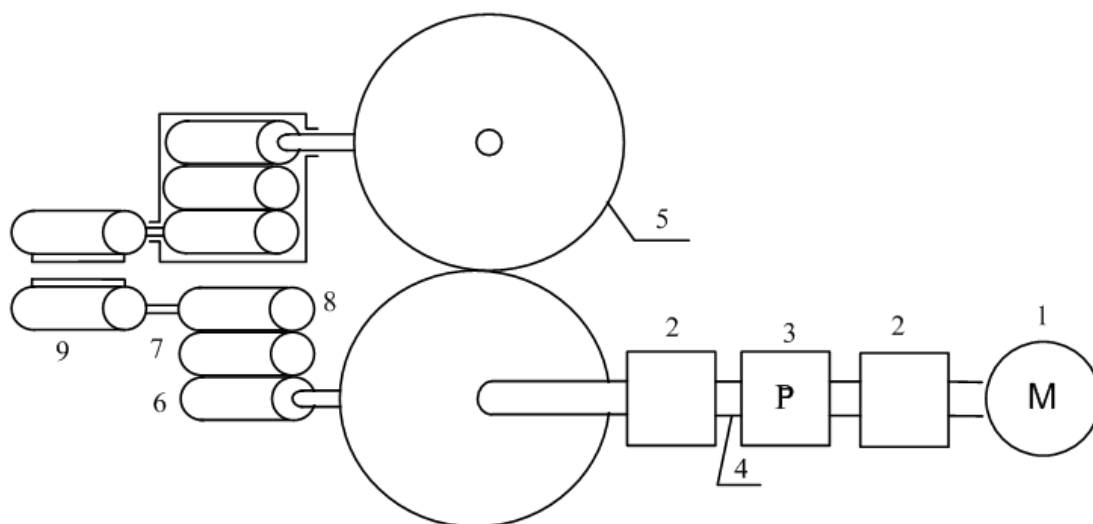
Кинематическая схема барабанных ножниц с поступательно движущимися ножами. 1 - двигатель; 2 - муфта; 3 - редуктор; 4 - вал; 5 - большая шестерня; 6 -солнечная шестерня, 7 - промежуточная шестерня; 8 - планетарная шестерня; 9 - ножи
